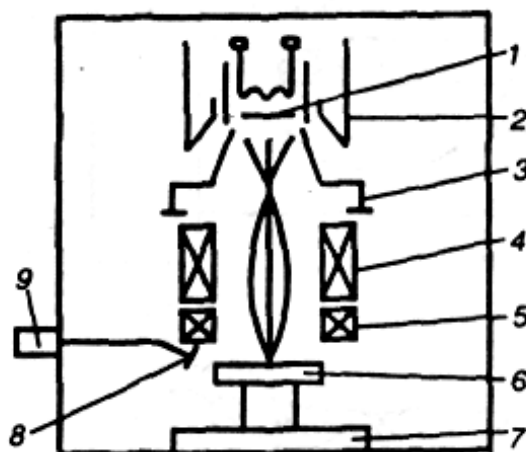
Схема для обработки и сварки с помощью электронного луча
